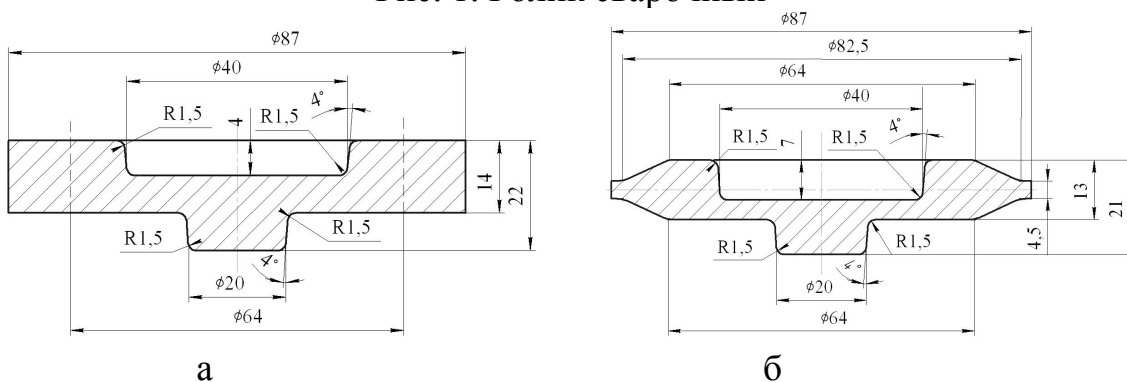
Заготовки детали «ролик сварочный»: а – до штамповки; б – после штамповки
